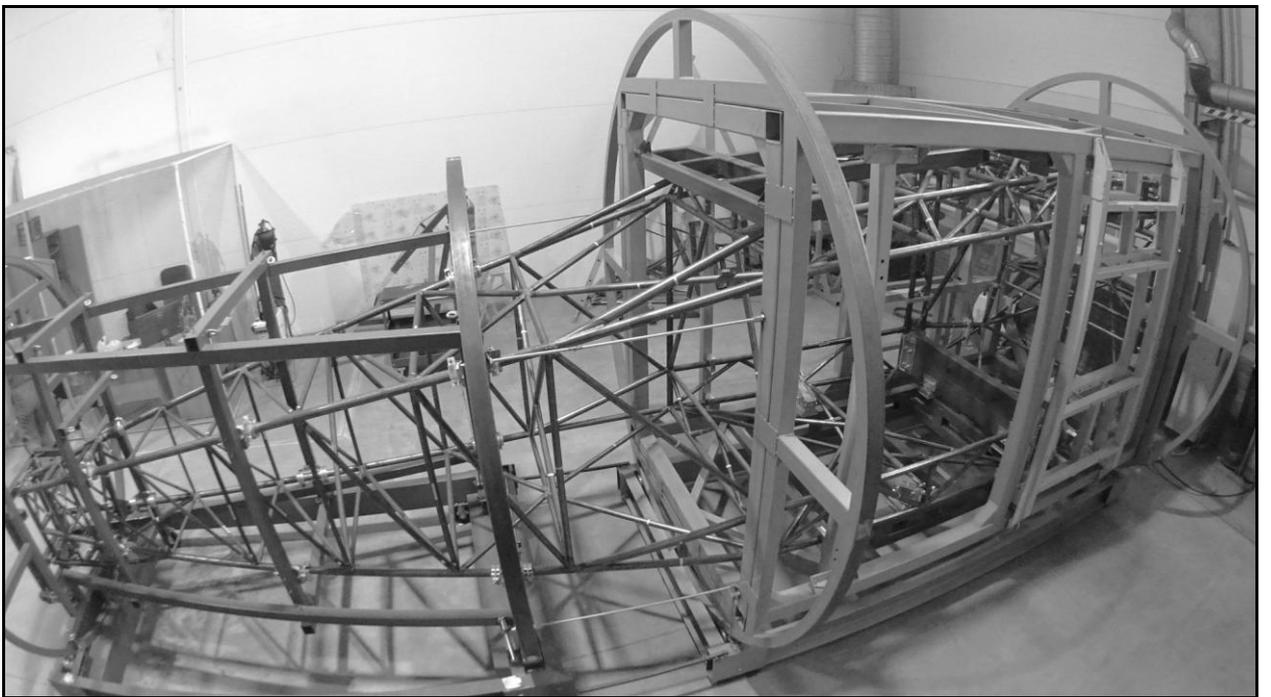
Сборка-сварка фермы в стапелях-кантователях.
